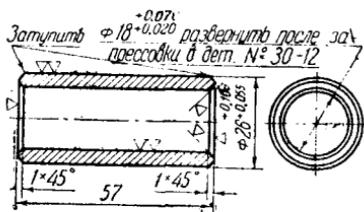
Дет. № 30-09. Втулка конической шестерни
